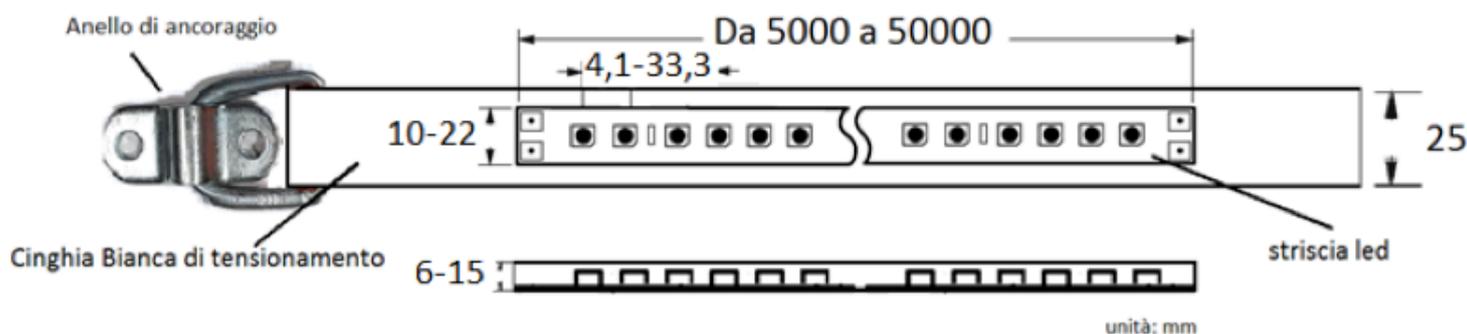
Anello di fissaggio in testa alla striscia led con due punti di fissaggio
